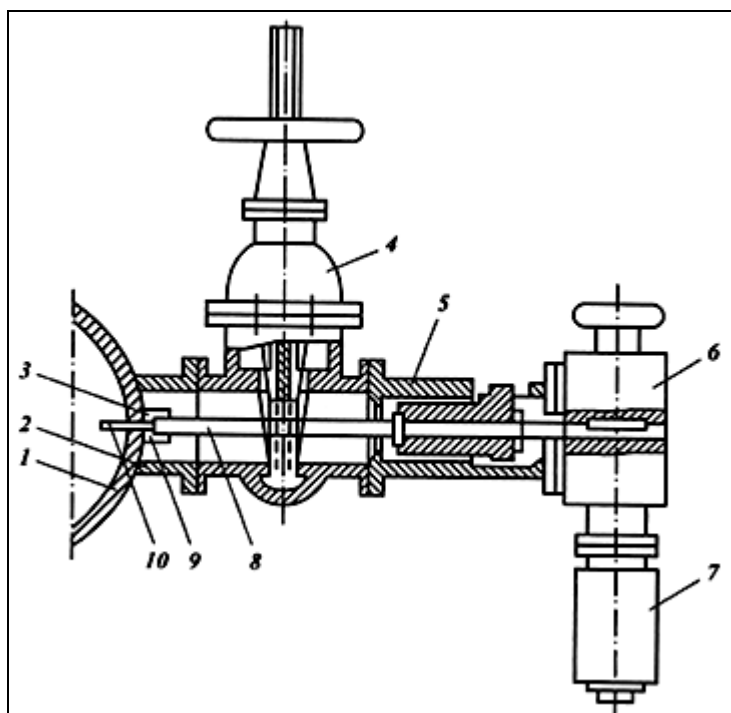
Приспособление для врезки в трубопровод: 1 - трубопровод; 2 - штуцер; 3 - держатель; 4 - задвижка; 5 - корпус устройства; 6 - редуктор; 7 - электродвигатель; 8 - шпиндель; 9 - резец; 10 – сверло
